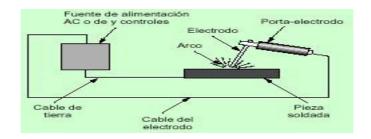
Esquema del proceso de soldadura eléctrica al arco
